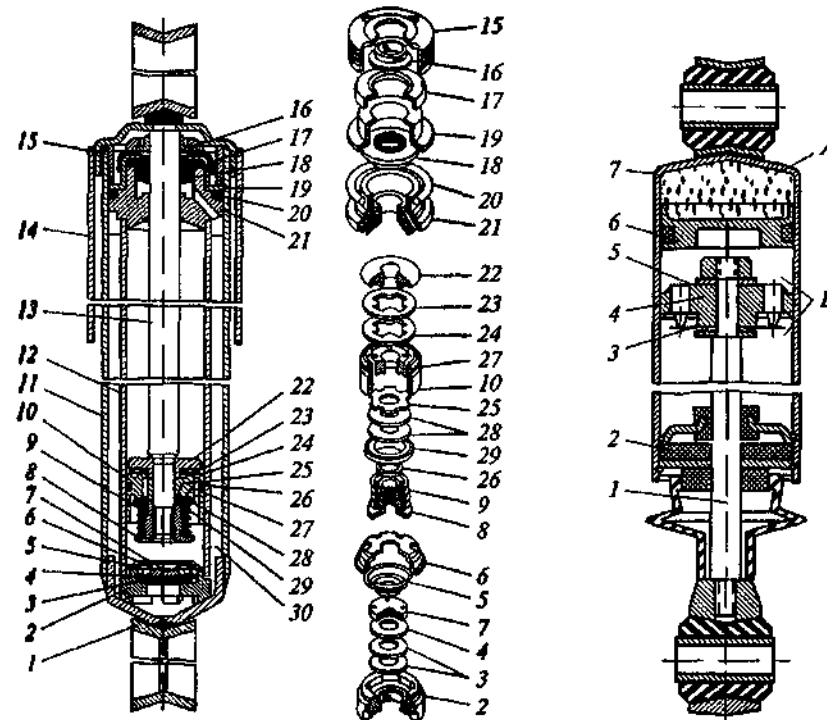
Гидравлический амортизатор / — проушина; 2 — днище; 3, 4, 25 и 28 — диски; 5, 9 и 23 — пружины; 6 и 19 — обоймы; 7 и 22 — тарелки, 8 и 15 — гайки; 10 — поршень; 11 — резервуар, 12 — цилиндр; 13 — шток; 14 — кожух; 16 и 27 — уплотнения; 17, 18 и 20 — уплотнения; 27 — манжета, 24 и 29 — клапаны; 26 — шайба; 30 — камера
